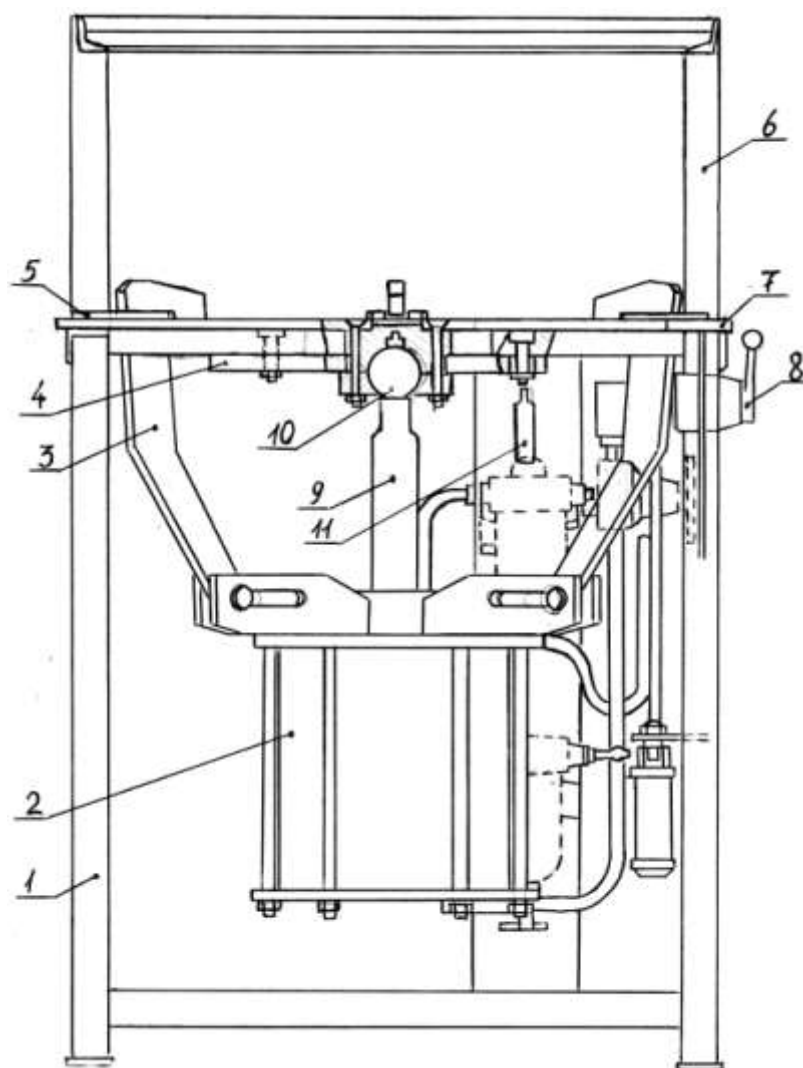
Стенд для разборки муфт сцепления.
